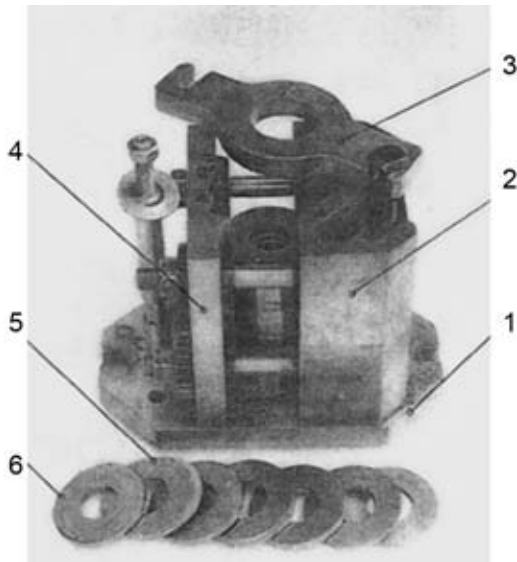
Установочное приспособление с набором колец: 1 — основание; 2 — призма; 3 — планка прижимная; 4 — плита прижимная; 5 — кольцо-выточка; 6 — кольцо-поясок
